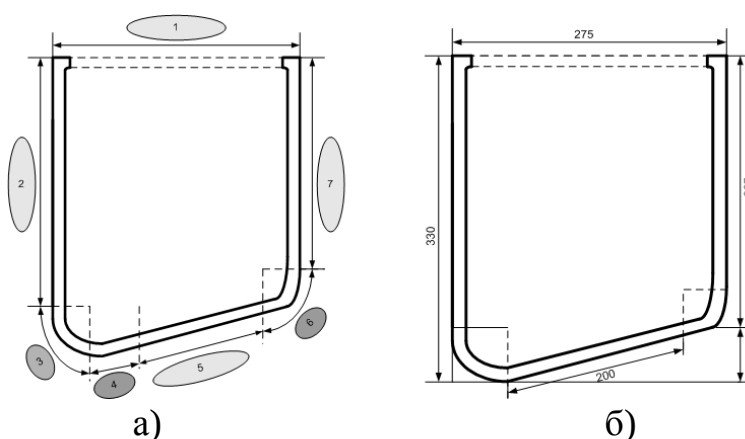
Половина індукційного каналу системи «індуктор – виток розплаву»: а – розбиття на ділянки для розрахунку активного опору (R_b), б – ескіз з основними розмірами
